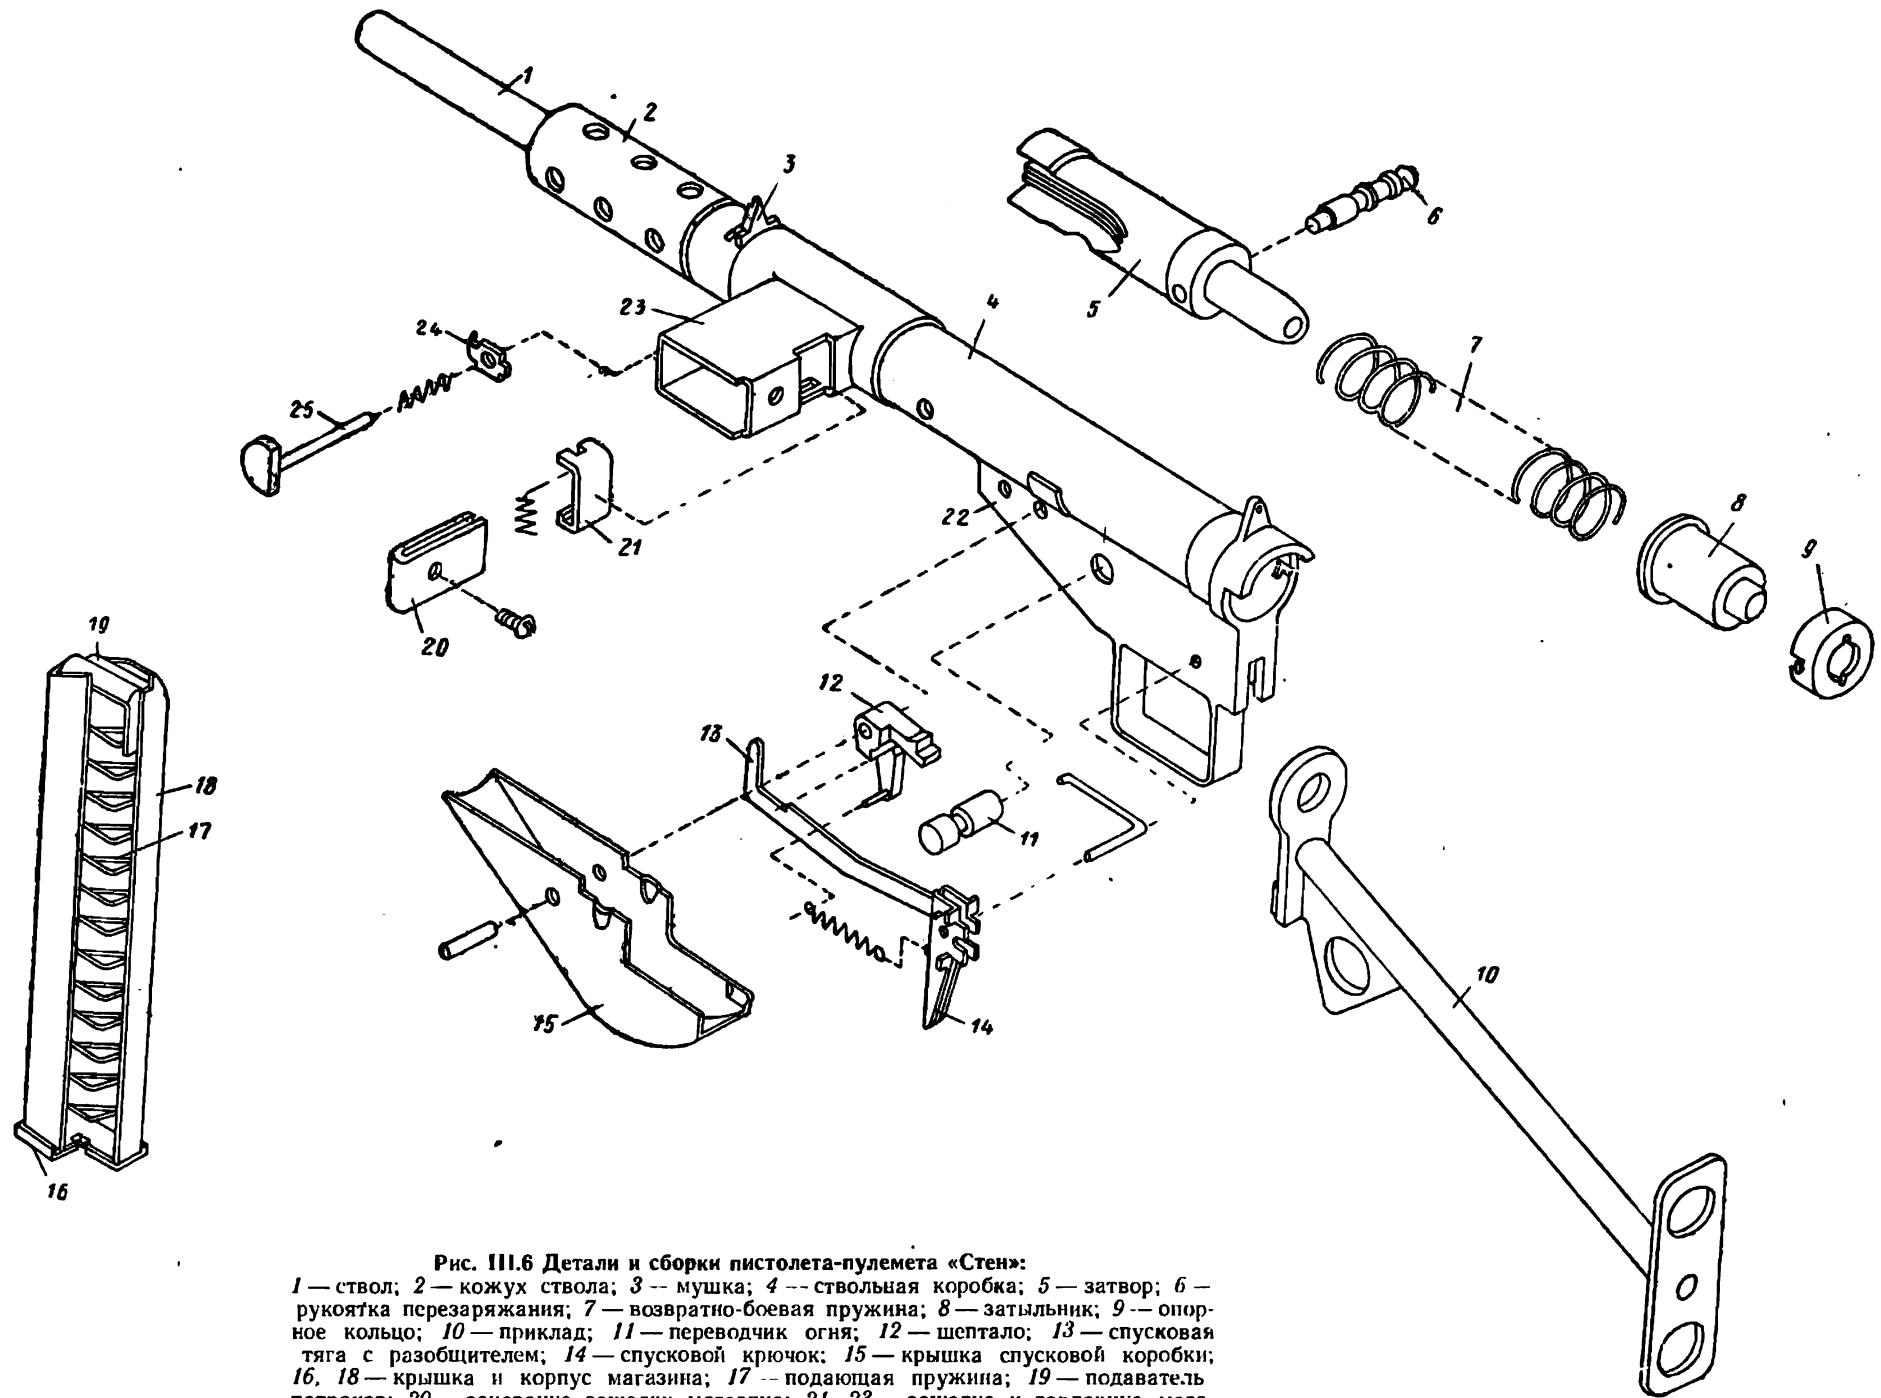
Детали и сборки пистолета-пулемета «Стен»:
